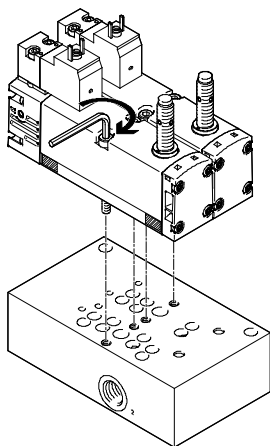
Befestigung der Magnetventile auf dem Steuerblock
